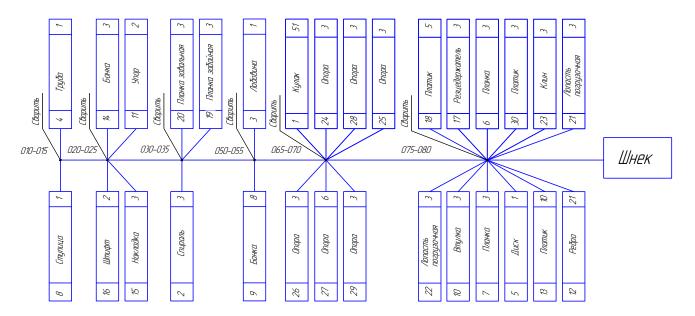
Технологическая схема изготовления шнека сварного
